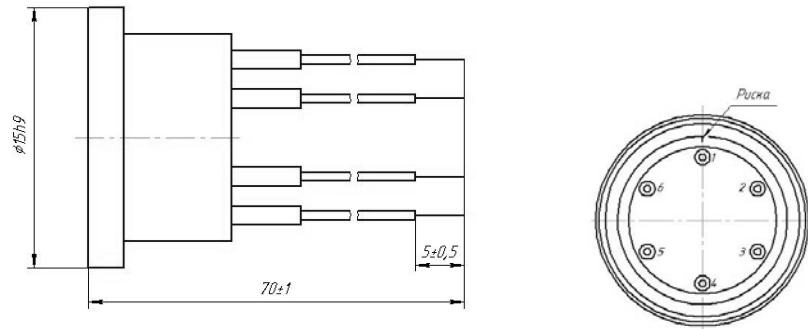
Балочный ЧЭ металлопленочного датчика
